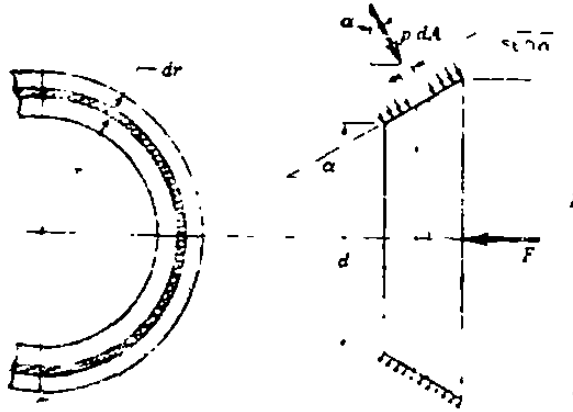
Designación de las dimensiones de un embrague de cono.
